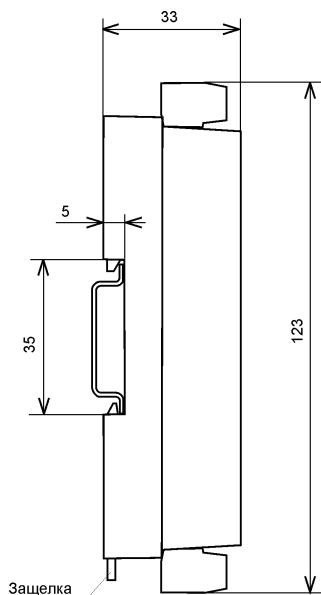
Габаритный чертеж модуля с креплением к DIN-рейке. Вид сбоку
